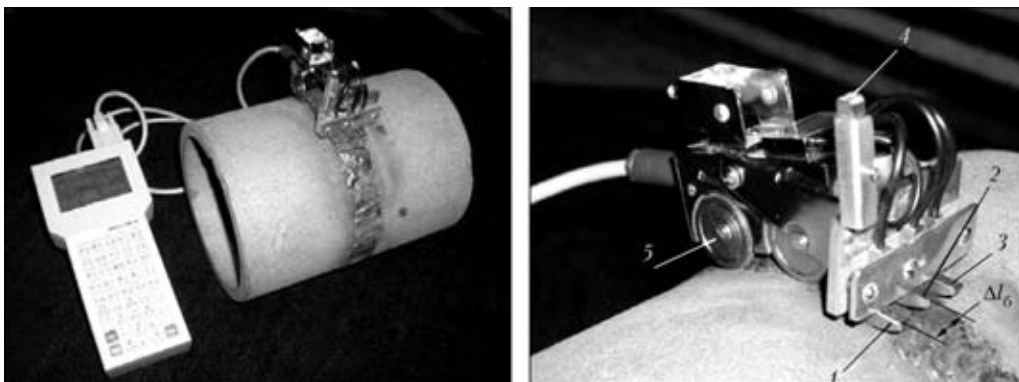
Контроль стыковых сварных соединений труб четырехканальным датчиком прибора ИКН-1М-4: 1–3 — феррозондовые преобразователи сканирующего устройства для регистрации поля H_p на поверхности сварного шва; 4 — феррозондовый преобразователь для отстройки от внешнего магнитного поля H_p ; 5 — колеса привода измерителя длины; ΔL_6 — базовое расстояние между феррозондовыми преобразователями
